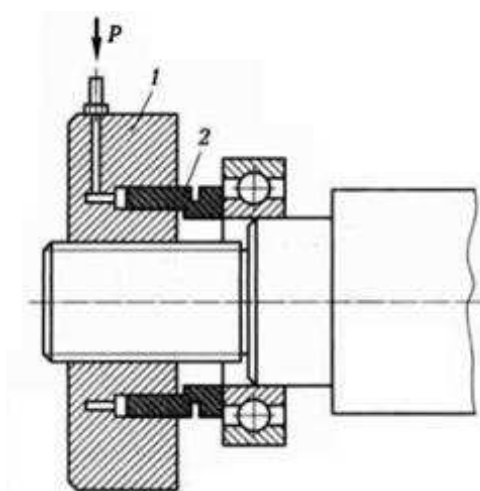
Гидравлическая гайка для запрессовки подшипников
